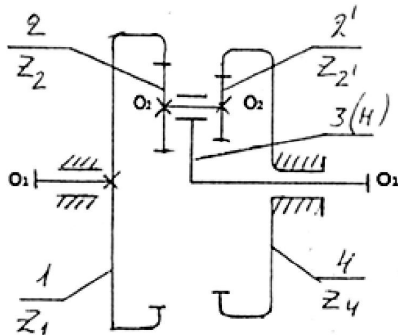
Схема 3. Планетарный механизм со сложным сателлитом и внутренними зацеплениями колес
